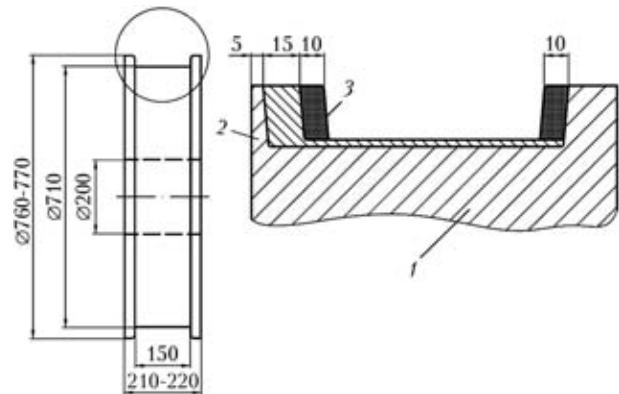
Схема наплавки крановых колес: 1 — основной металл; 2, 3 — наплавленный металл, полученный с использованием проволок соответственно ВЕЛТЕК-Н300РМ и ВЕЛТЕК-Н280РМ
